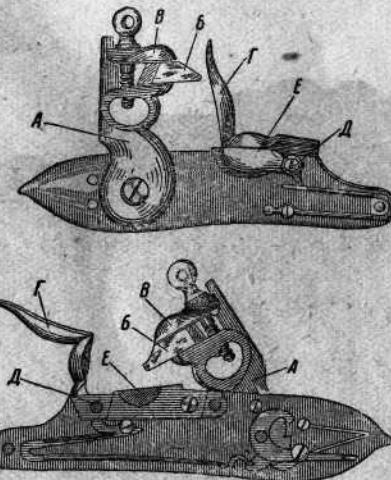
Ударный кремневый замок позднейшего времени для военных ружей и пистолетов: на верху — наружный вид (курок взведен, полка накрыта крышкой-огнивом); внизу — вид с внутренней стороны (виден механизм; курок спущен, крышка-огниво откинута).
